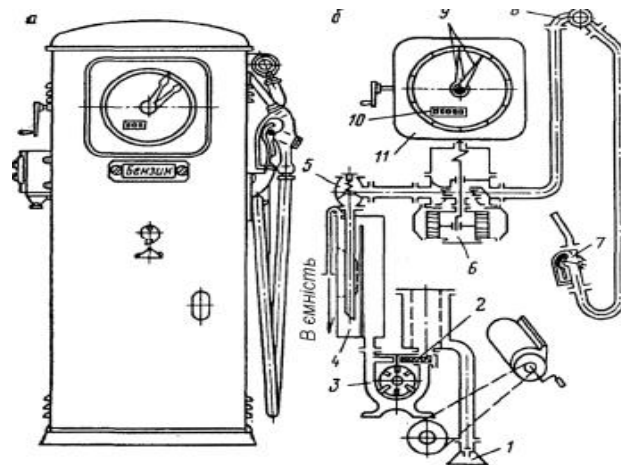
Загальний вид (а) і технологічна схема (б) паливороздаточної колонки КЕР-40-0,5-1
